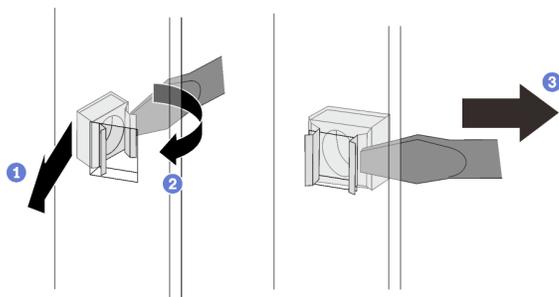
Installazione di dadi a gabbia con un cacciavite a testa piatta
